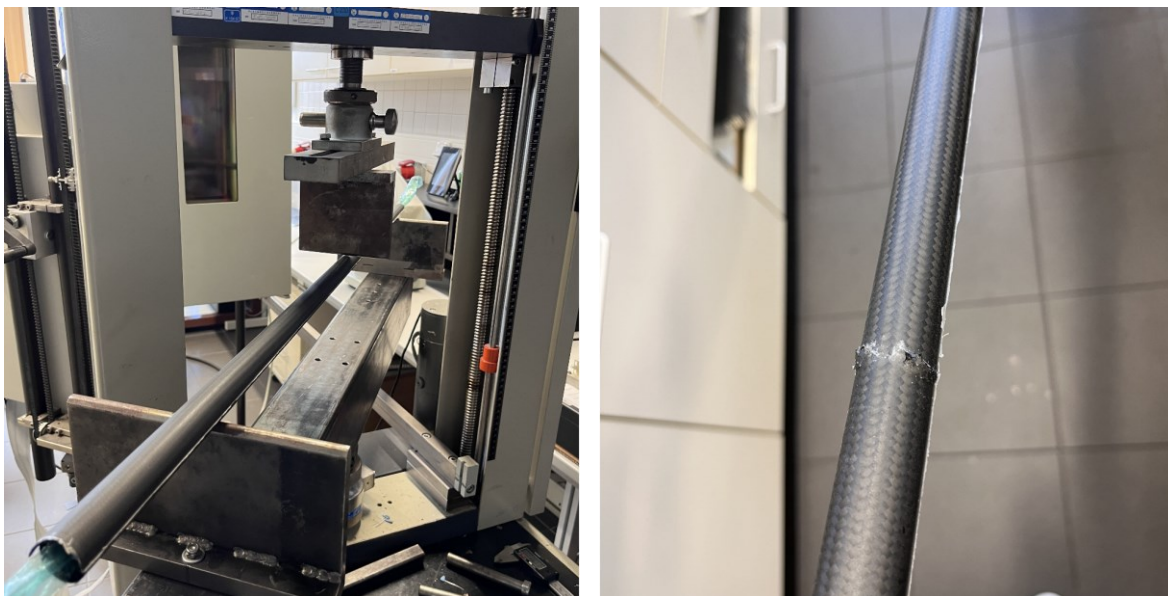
Testování čtvrtého prototypu (vlevo), místo zlomu (vpravo)
